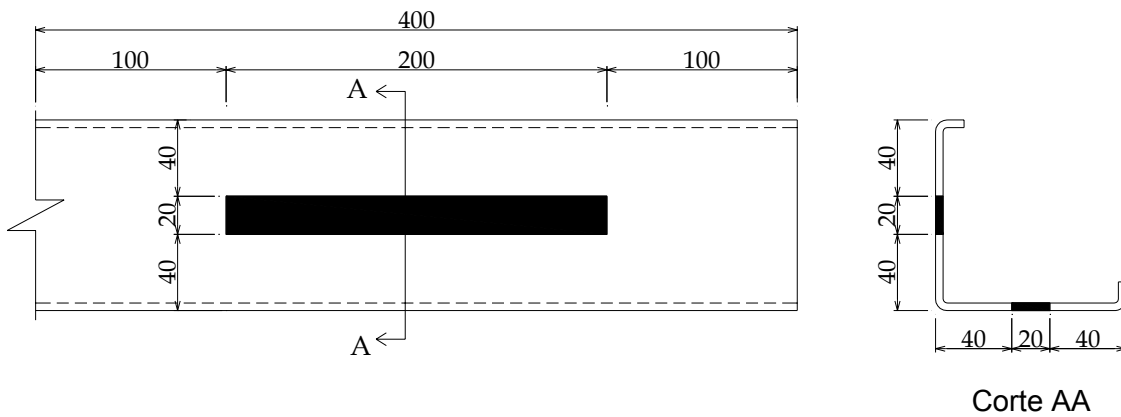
Localização dos corpos-de-prova na barra: perfil Le 100x15x1,50 (dimensões em mm)
